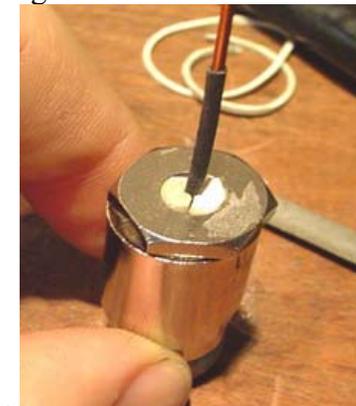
Conector N-hembra, rearmado y con el pin central soldado al alambre de cobre.
